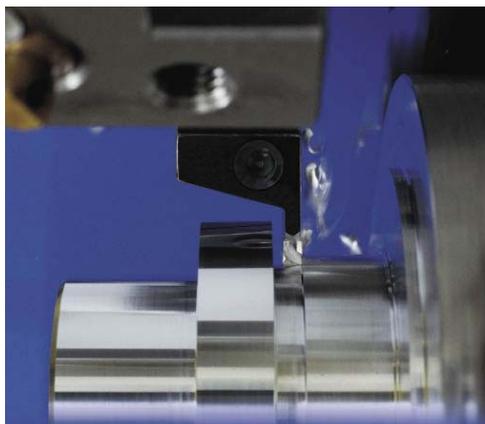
Инструмент для точения канавок с пластиной из КНБ.
